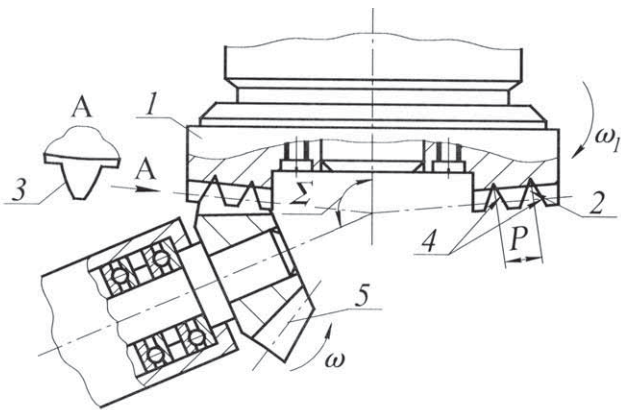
Схема шевингования-прикатывания конических зубчатых колес: 1 – шевер-прикатник; 2 – стружечная канавка; 3 – боковые поверхности зубьев; 4 – режущие кромки; 5 – заготовка
